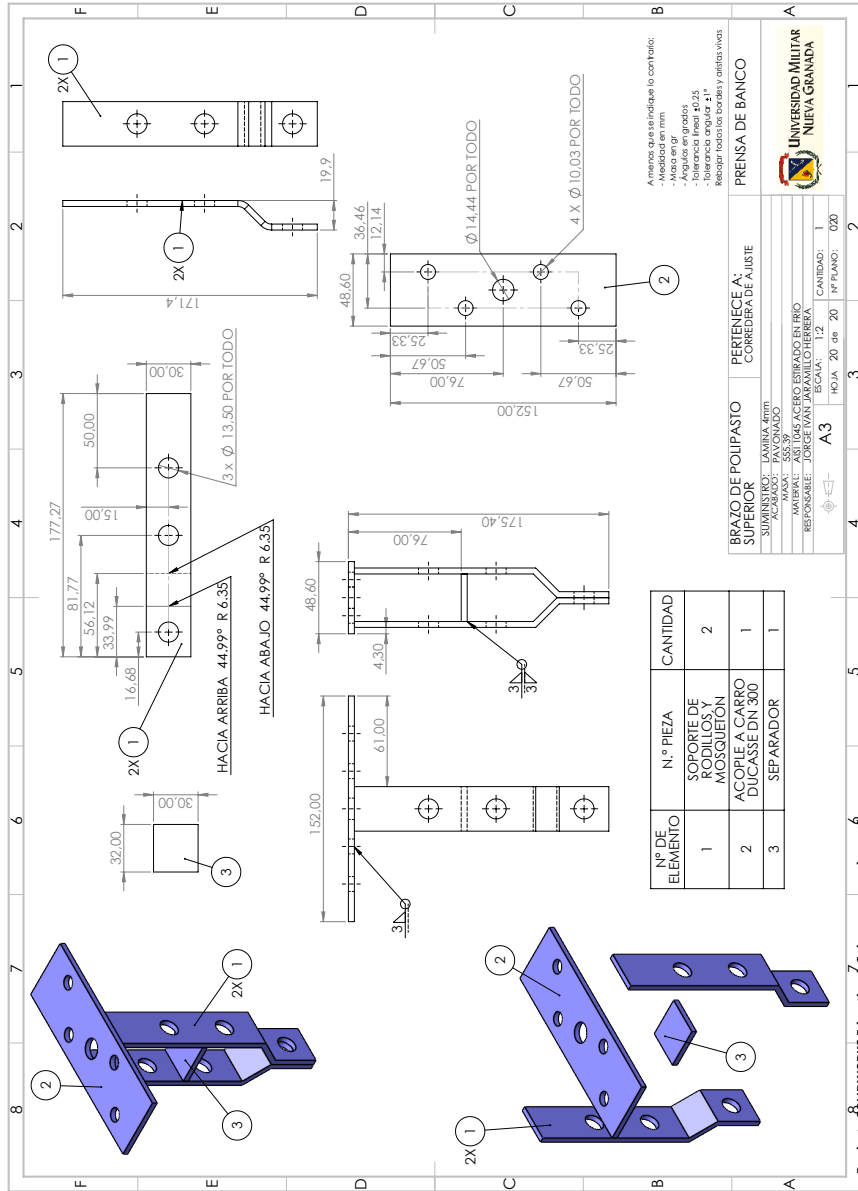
Plano 020, de la pieza "Brazo de Polipasto Superior". Modelo CAD y plano elaborado por el autor mediante la herramienta de pieza y dibujo de "Solidworks".
